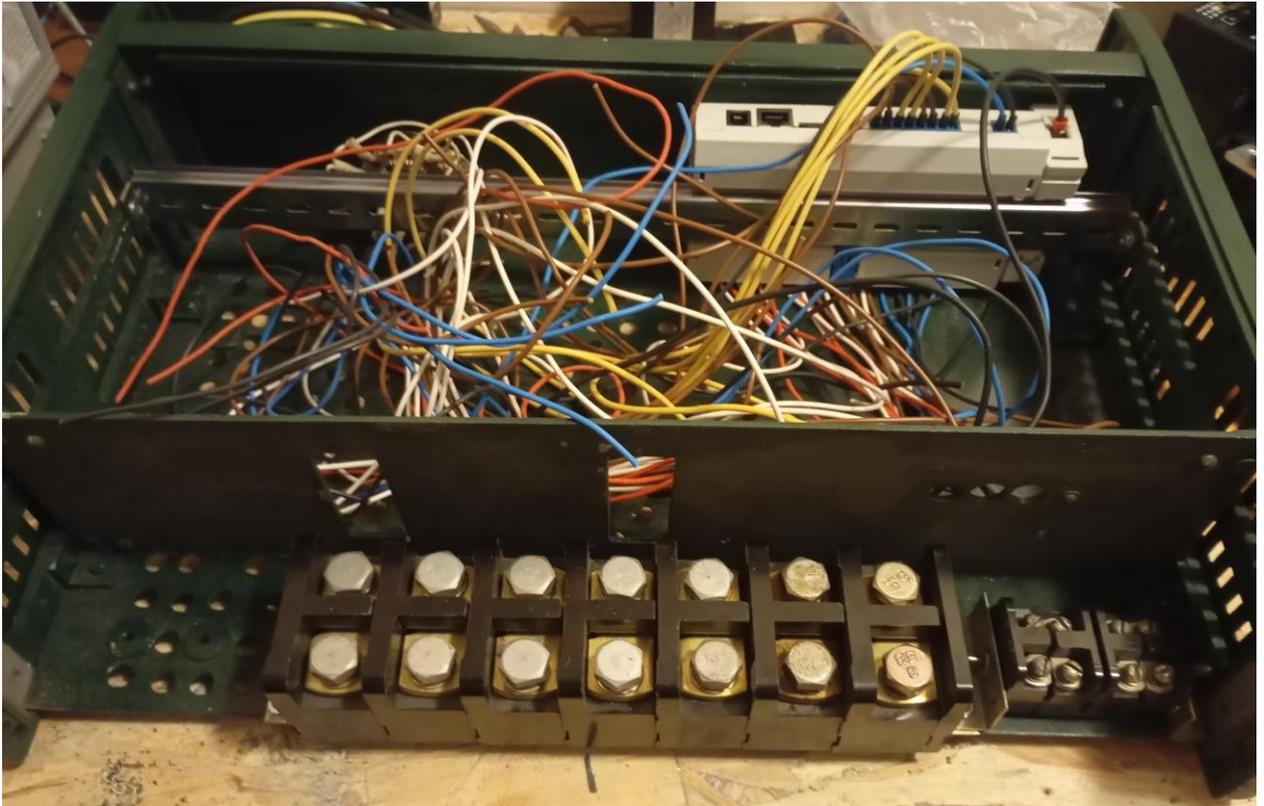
Зовнішній вигляд монтажного корпусу зі встановленими клемними затискачами
